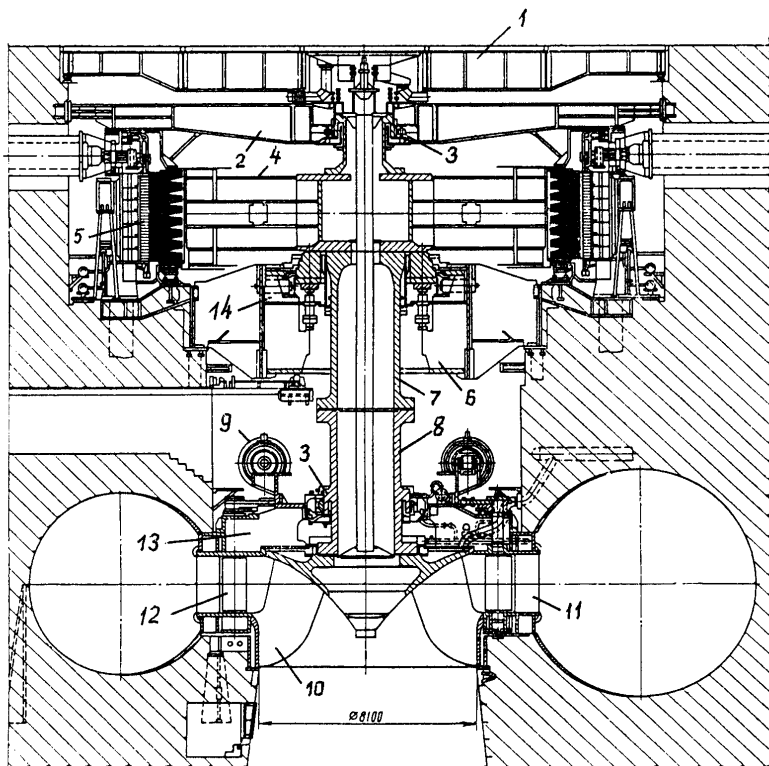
Гидроагрегат ГЭС Итайпу на р. Парана (Бразилия-Парагвай) зонтичного типа с опорой на нижнюю крестовину ($H = 118$ м; $f = 60$ Гц; $P = 700$ МВт; $\cos \phi = 0,95$; $n = 92,3$ об/мин): 1, 2 — верхняя крестовина; 3 — направляющий подшипник; 4 — ротор генератора; 5 — сердечник статора с силовыми обмотками; 6 — кольцевая конструкция нижней крестовины; 7 — вал генератора; 8 — вал турбины; 9 — сервомотор; 10 — рабочее колесо турбины; 11 — статор турбины; 12 — лопатка направляющего аппарата; 13 — крышка турбины; 14 — подпятник
